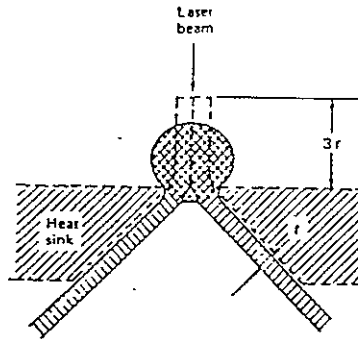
Soldadura de láser formando una esquina. Note la recomendación de penetración de calor y las dimensiones para lograr que la esquina sea una barra de soporte.
